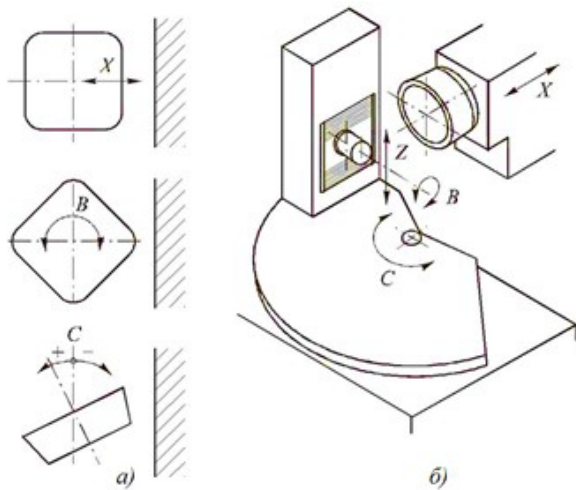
Схема шлифования задних поверхностей МТП на станке с ЧПУ: а — главные формообразующие движения; б — данные движения на станке
